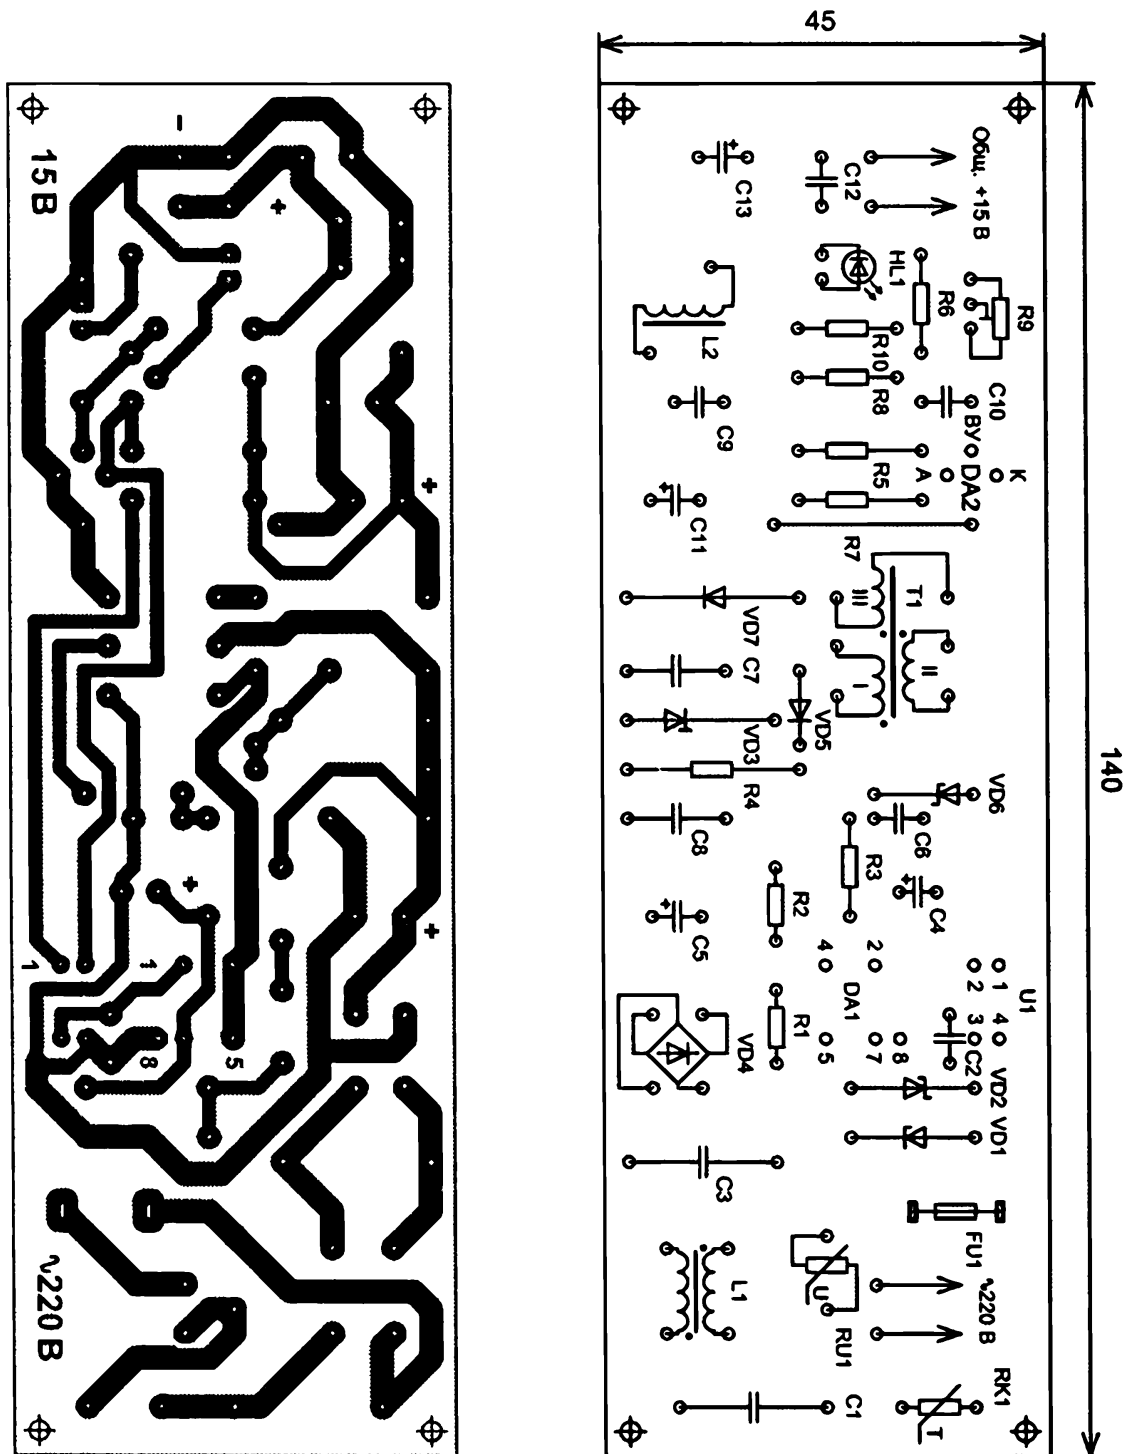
Чертеж печатной платы и сборочный чертеж
